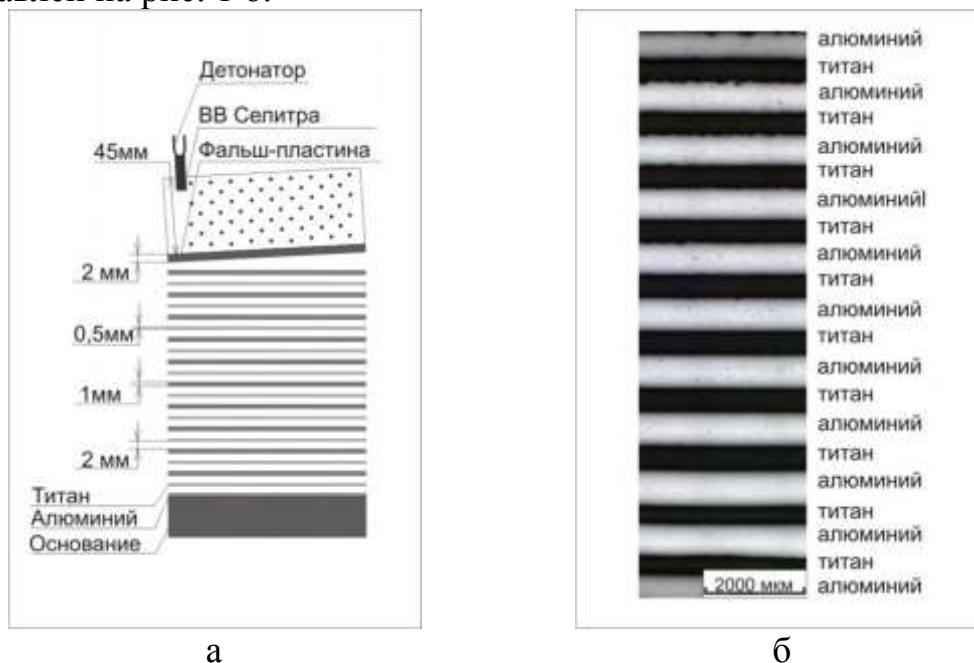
Схема получения 21-слойного композита методом сварки взрывом (а) и общий вид композита в поперечном сечении (б).
